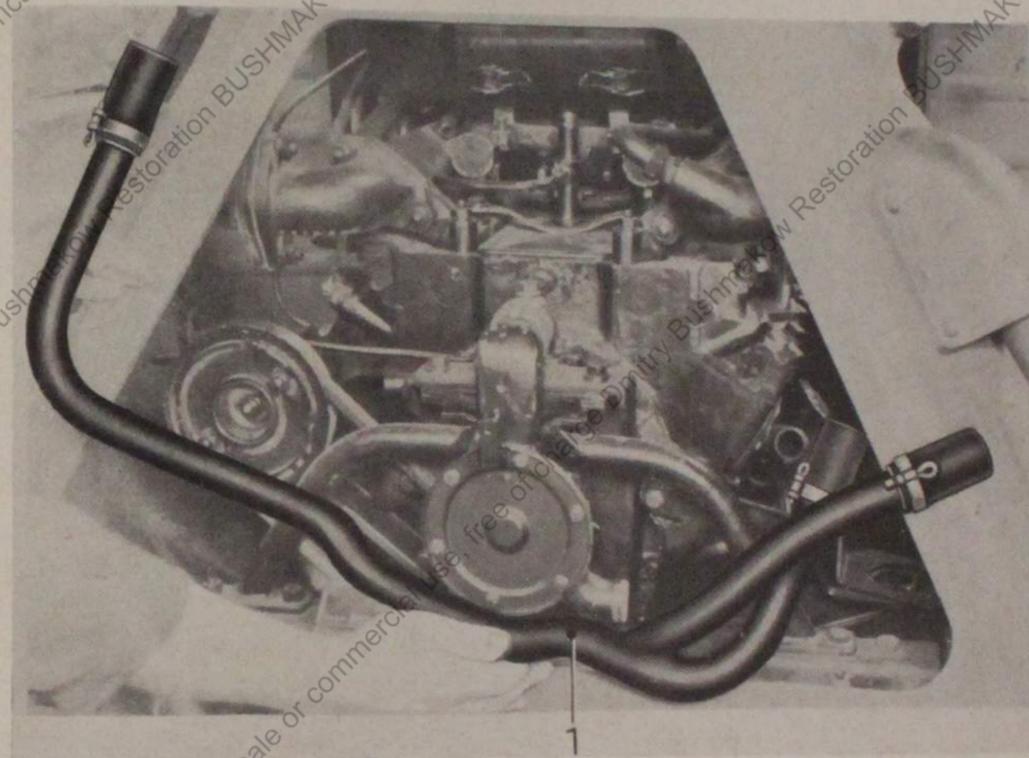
Verbindungsrohr für Kernlochdeckel einbauen
